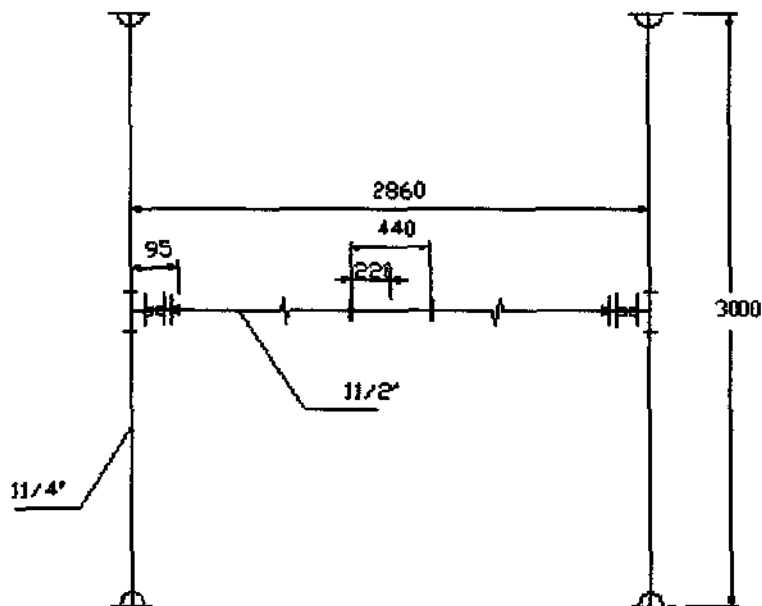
Desenho representativo das dimensões da Estrutura "H"
